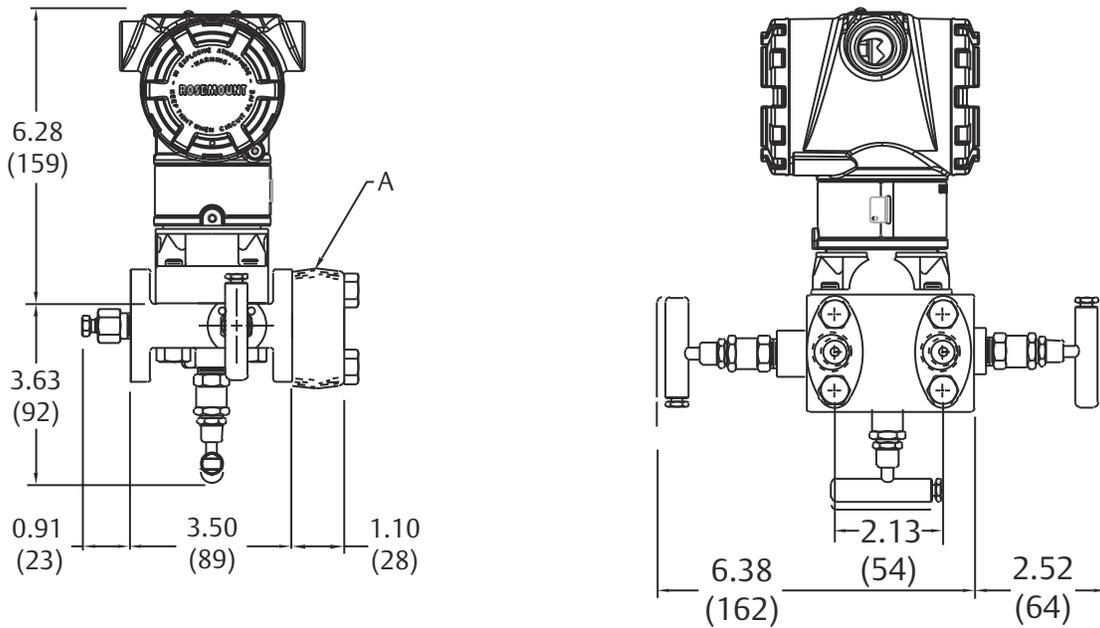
Rosemount 3051C Coplanar mit Anpassungsflansch
